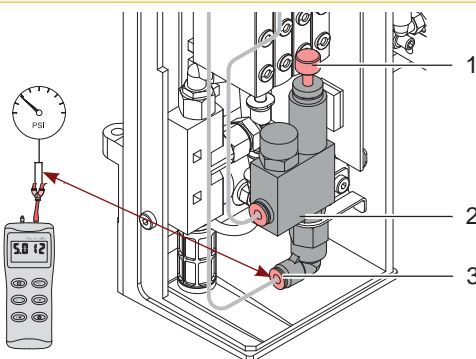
Druckminderventil Zylinder Z Ausfahrbewegung
